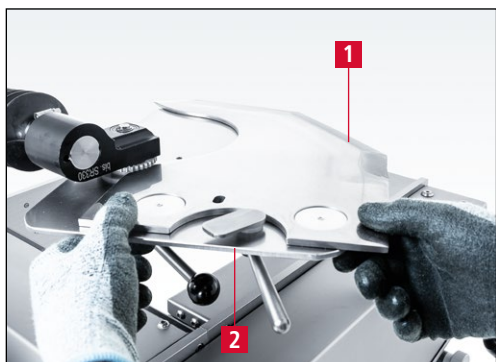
Fijación de la cuchilla en la placa de afilado
